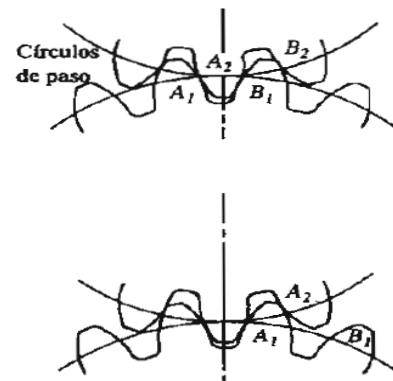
Ciclo de engranado de los dientes de los engranes [16]
